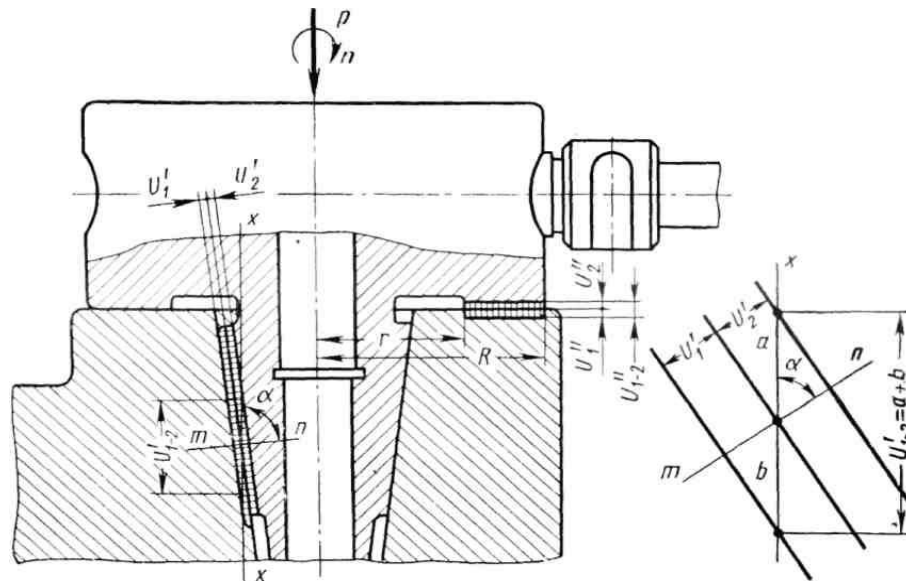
Схема для визначення зносу опор револьверної головки
